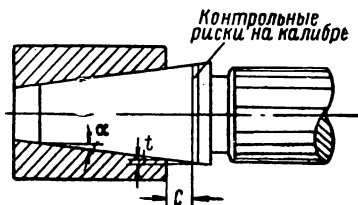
Схема проверки калибром конусного отверстия, размеры которого меньше заданных.
